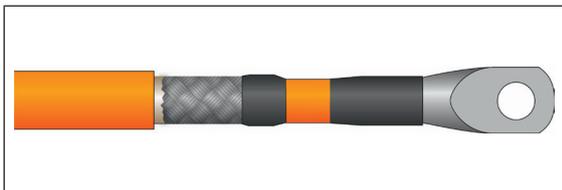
Schritt 8: Schrumpfschlauch platzieren und fixieren
